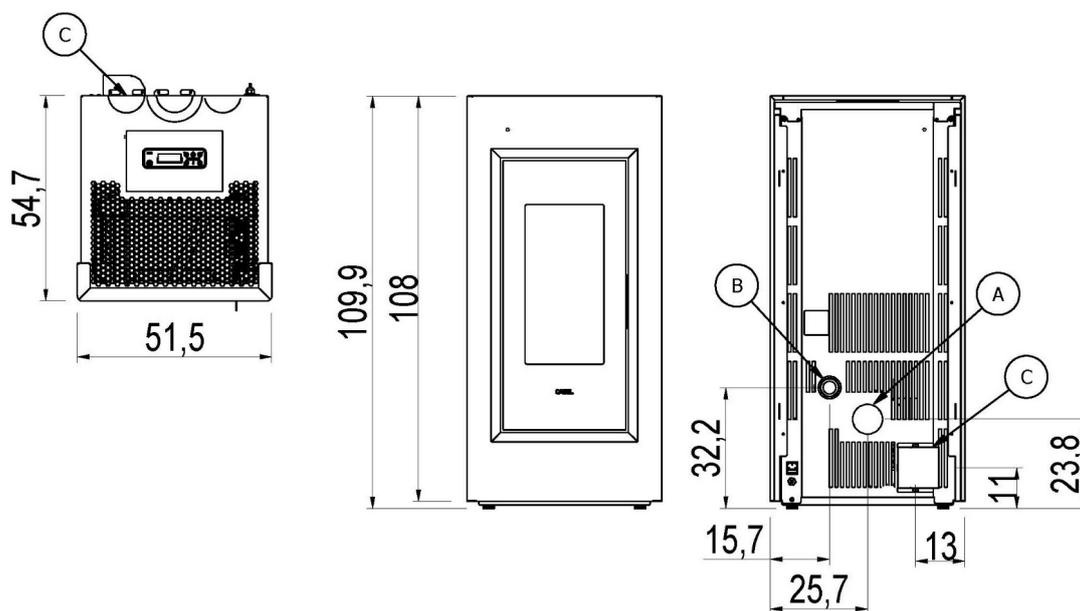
Dimensiones generales: Prince 11 - Prince Plus 11
